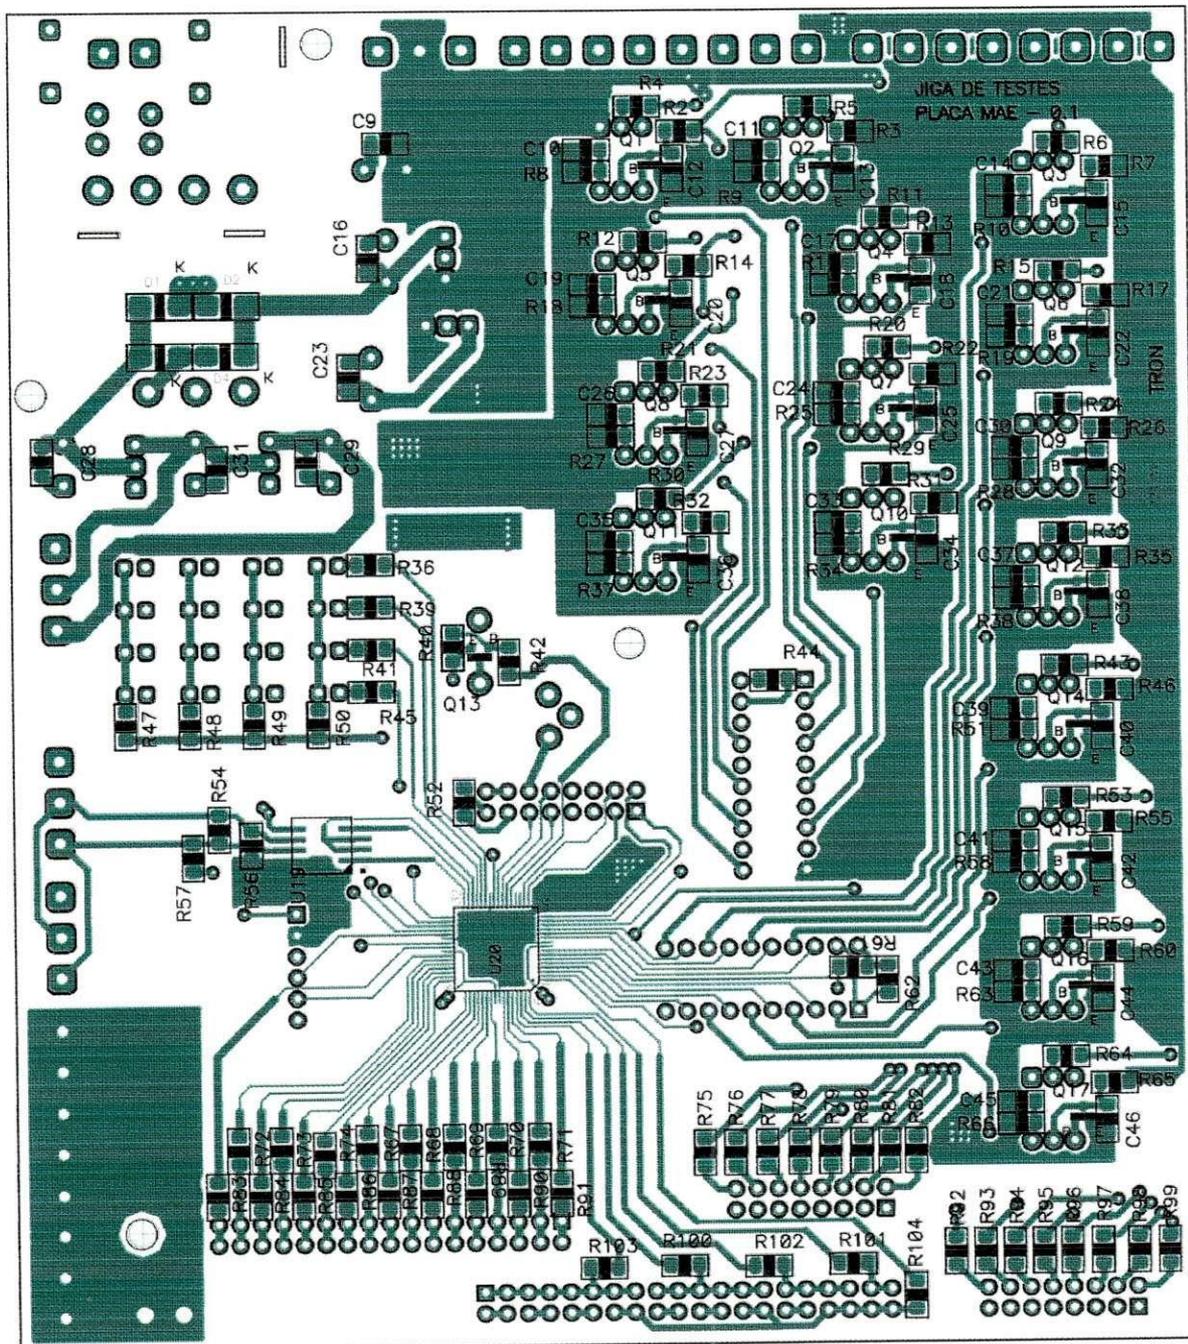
Placa Mãe - Face da Solda e dos Componentes SMD
